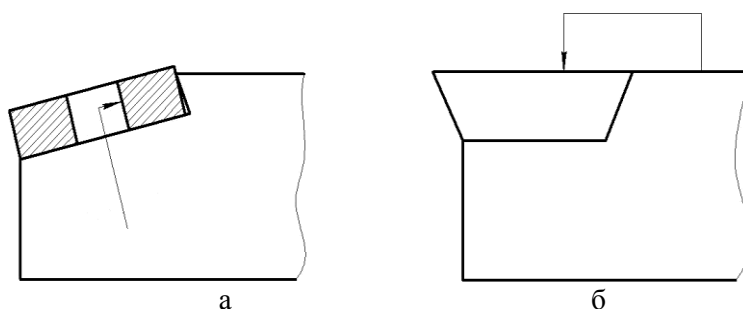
Схемы базирования и крепления СМП в корпусе резца:
